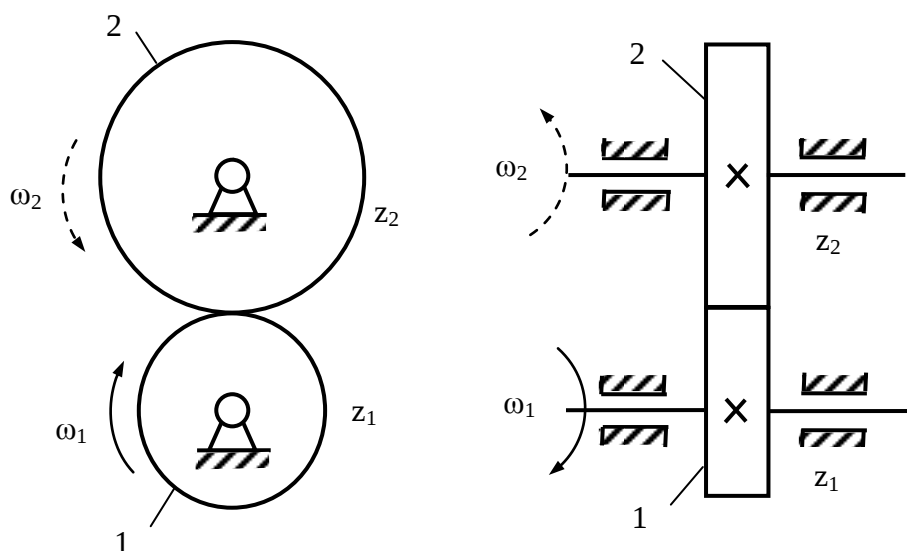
Схема одноступенчатой прямозубой цилиндрической передачи внешнего зацепления
